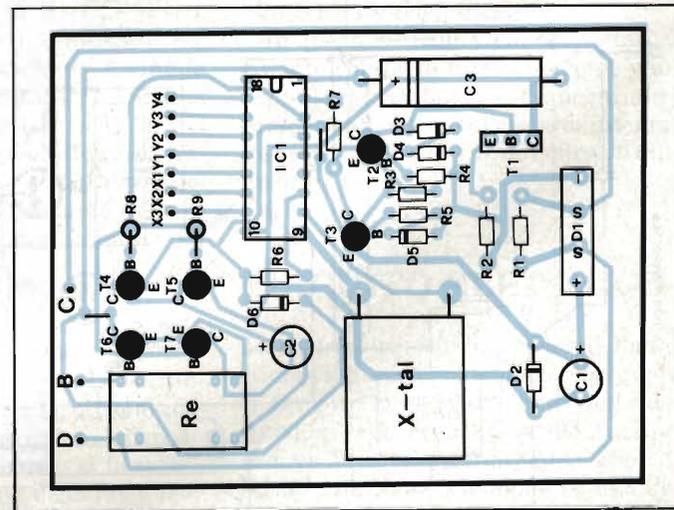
Disposizione dei componenti sul circuito stampato di fig. 6.
